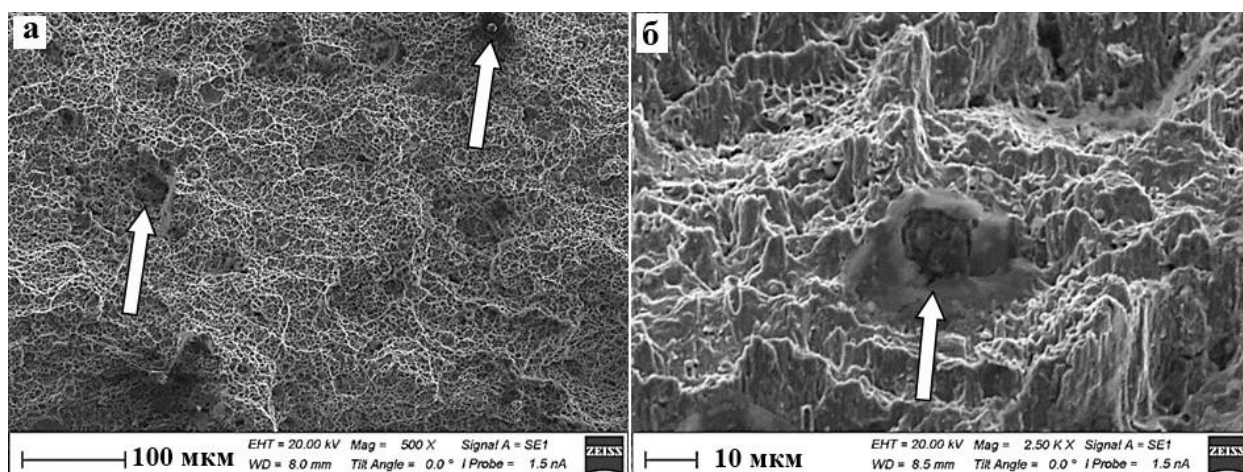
Поверхность вязкого излома металла сварного шва №2
